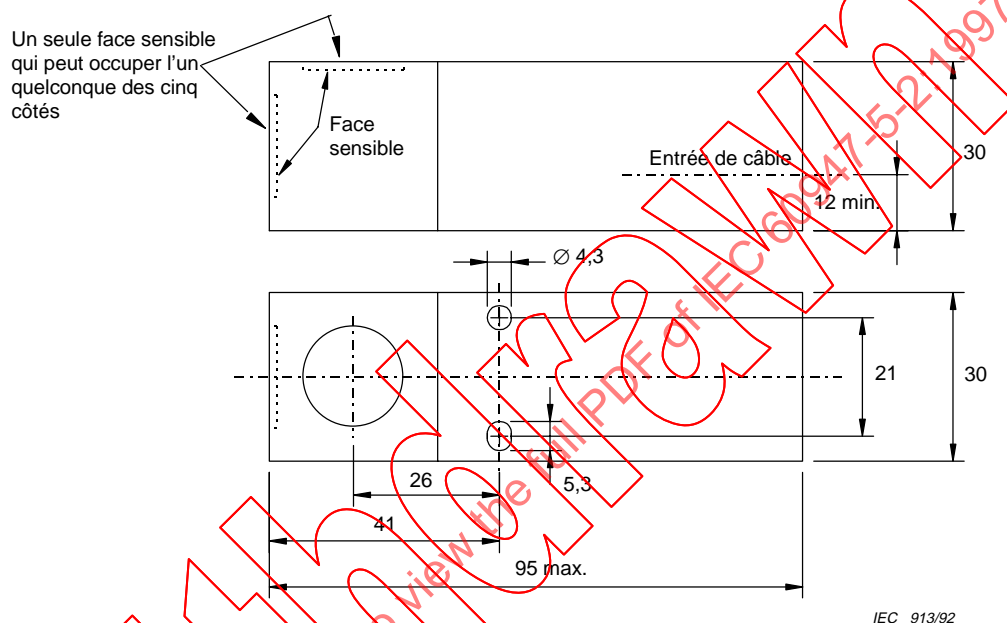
(CC) a – Dimensions, type C30 en millimètres
